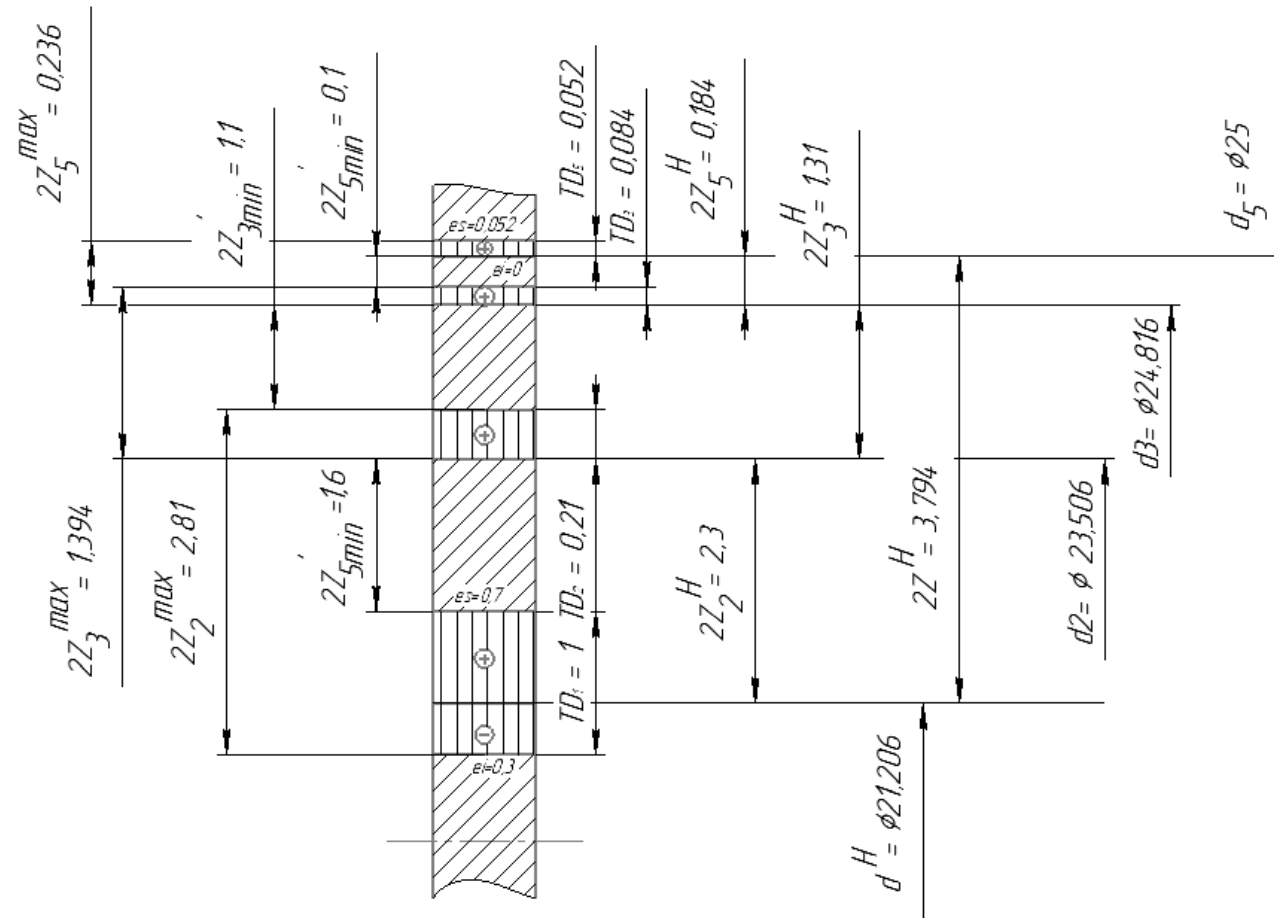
Розрахункова схема припусків для внутрішньої циліндричної поверхні $\phi 25^{+0,052}$
